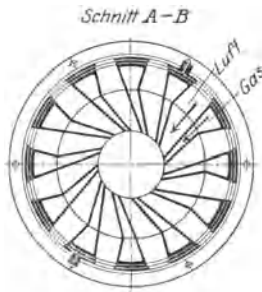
Moll-Torsions-Gasbrenner, Ausführung Balcke, Bochum.
